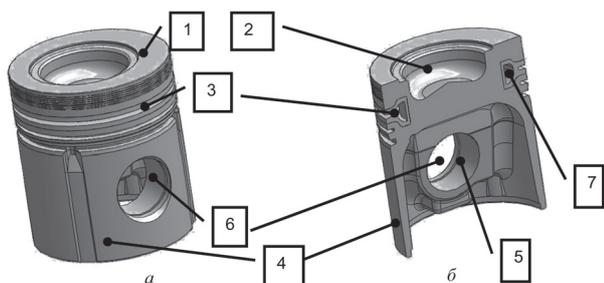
Общий вид поршня: а – поршень без разреза; б – разрез поршня; 1 – головка поршня; 2 – камера сгорания; 3 – нирезистовая вставка под верхнее поршневое кольцо; 4 – юбка поршня; 5 – бобышка под поршневой палец; 6 – отверстие под поршневой палец; 7 – полость для масляного охлаждения
